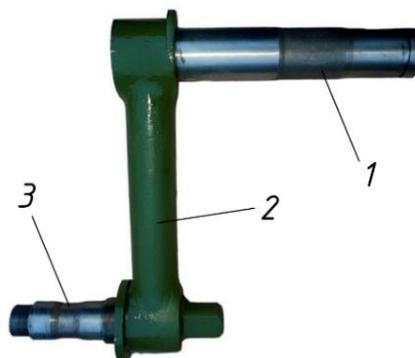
БМД-1 и Балансир: 1 – ось балансира; 2 – рычаг; 3 – ось катка
